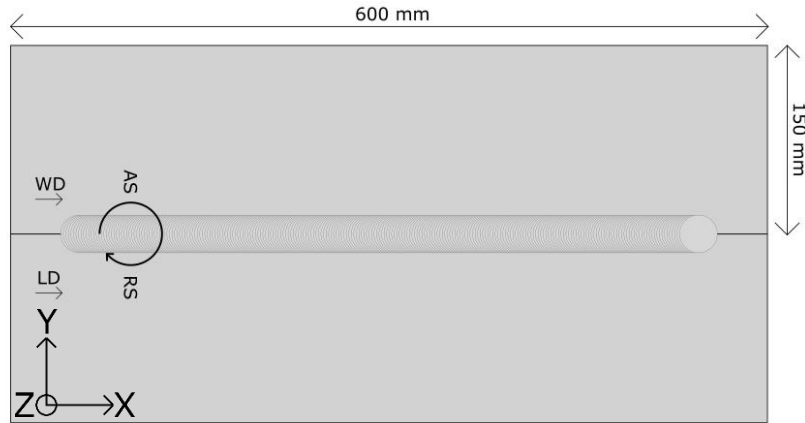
Schéma des plaques soudées par FSW, WD correspond à la direction de soudage et LD à la direction de laminage
